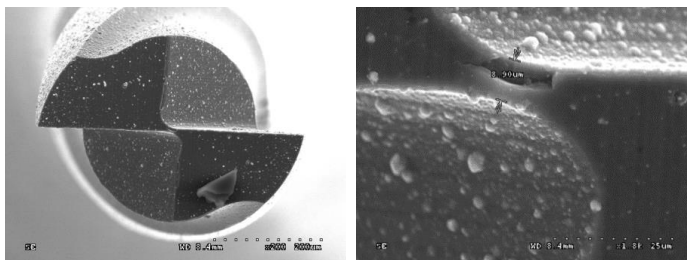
Die Bedeutung der Werkzeugprüfung vor der Bearbeitung. Diese Bilder zeigen einen Fehler am Fräskopf
